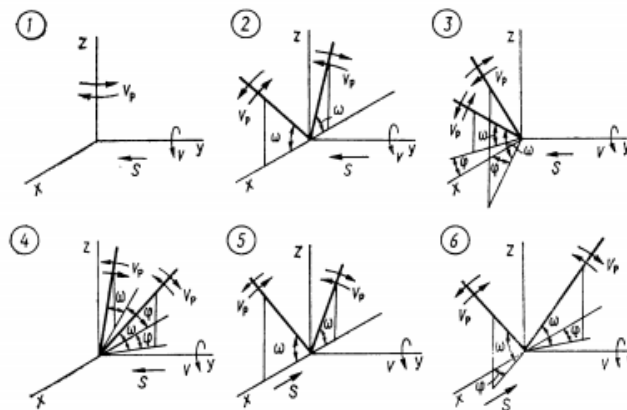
Кінематичні схеми різання ротаційного інструмента [9]
